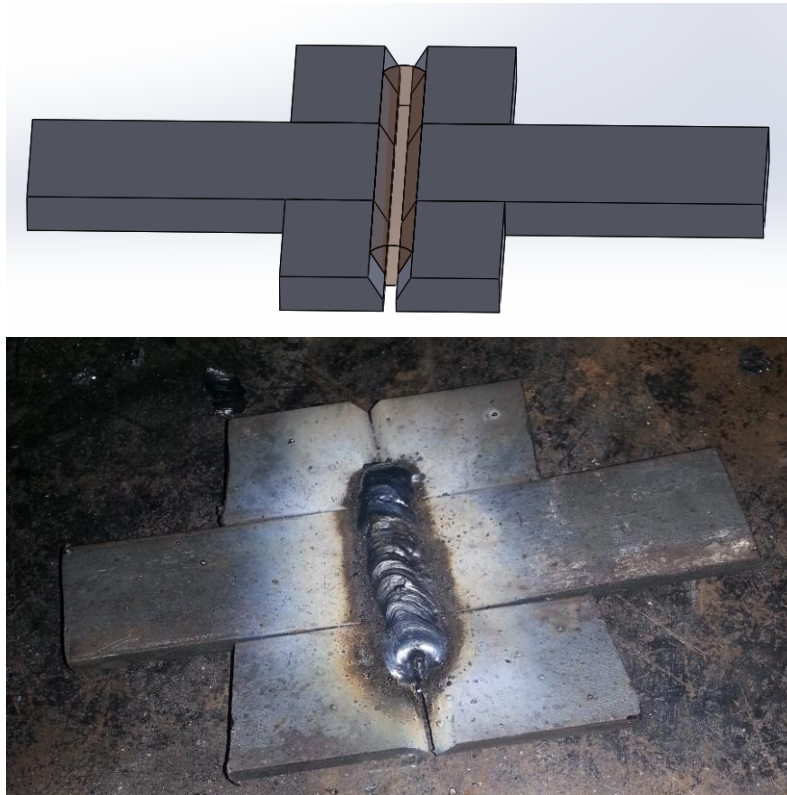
Proceso de soldadura de probeta.
